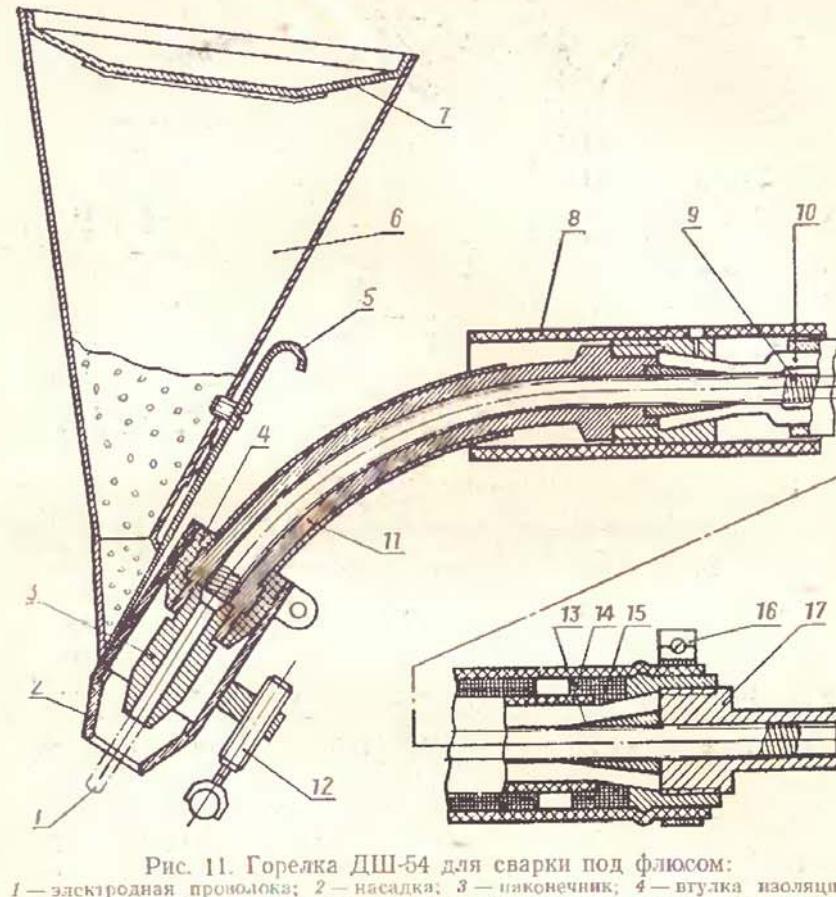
Горелка ДШ-54 для сварки под флюсом:
